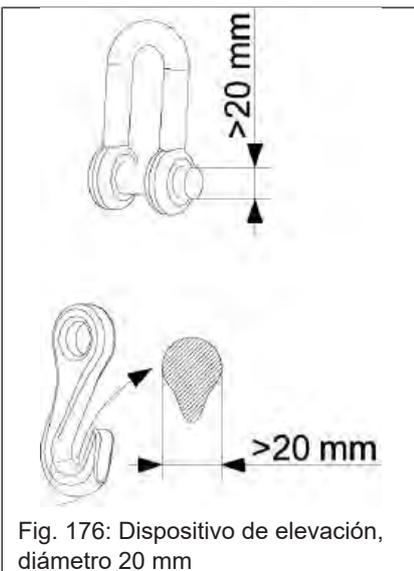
Dispositivo de elevación, diámetro 20 mm
